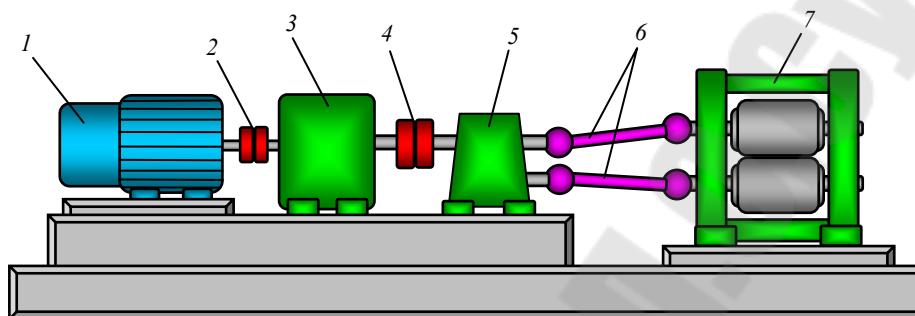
Главная линия одноклетьевого двухвалкового прокатного стана: 1 — электродвигатель; 2 — муфта моторная; 3 — редуктор; 4 — муфта коренная; 5 — шестеренная клеть; 6 — шпиндель; 7 — прокатная клеть.
